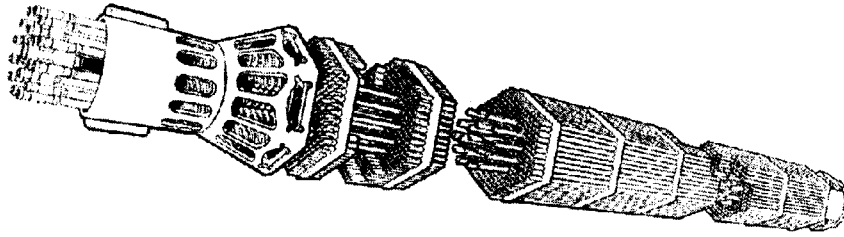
Вид топливной сборки реактора ВВЭР-1000
